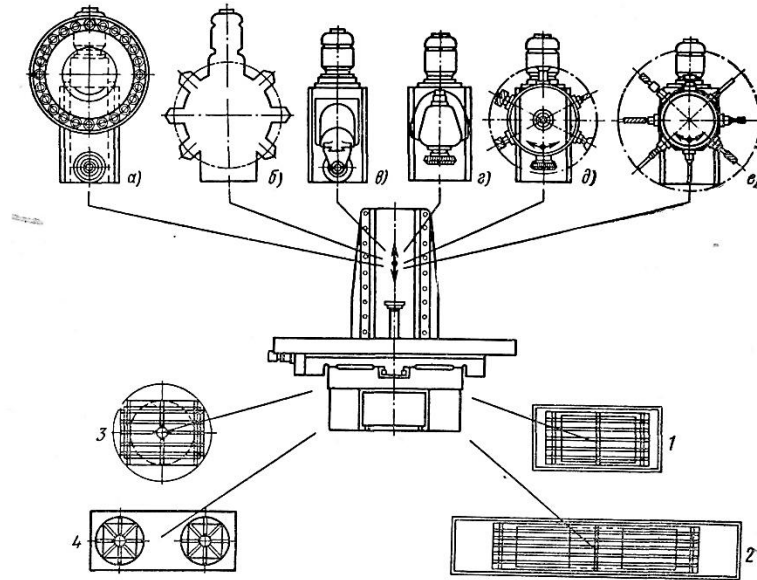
Схема компонування багатоопераційного верстата на принципах агрегування:
